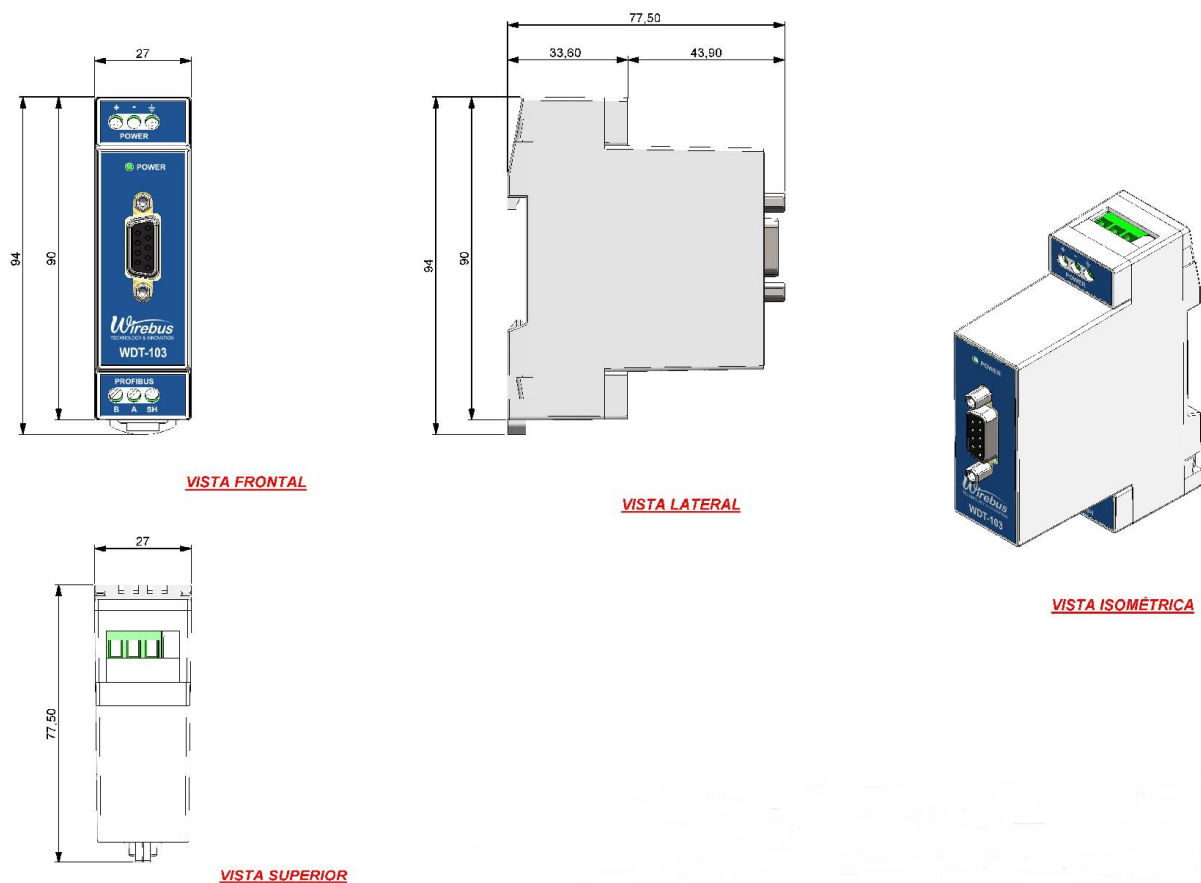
Dimensionamento para montagem (Cotas em milímetros)
